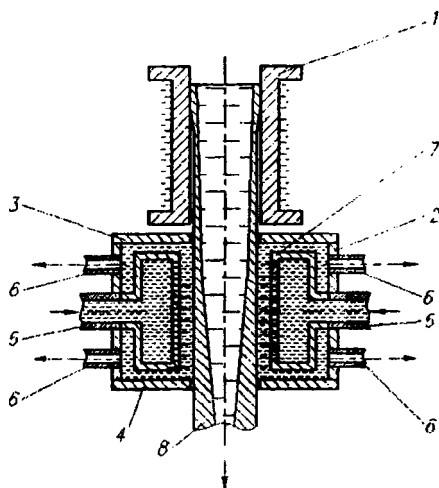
Схема устройства затопленно-струйного охлаждения непрерывнолитого слитка: 1 – кристаллизатор; 2 – кожух; 3 – фланец верхний; 4 – фланец нижний; 5 – патрубок подводящий; 6 – патрубок отводящий; 7 – коллектор; 8 – слиток
